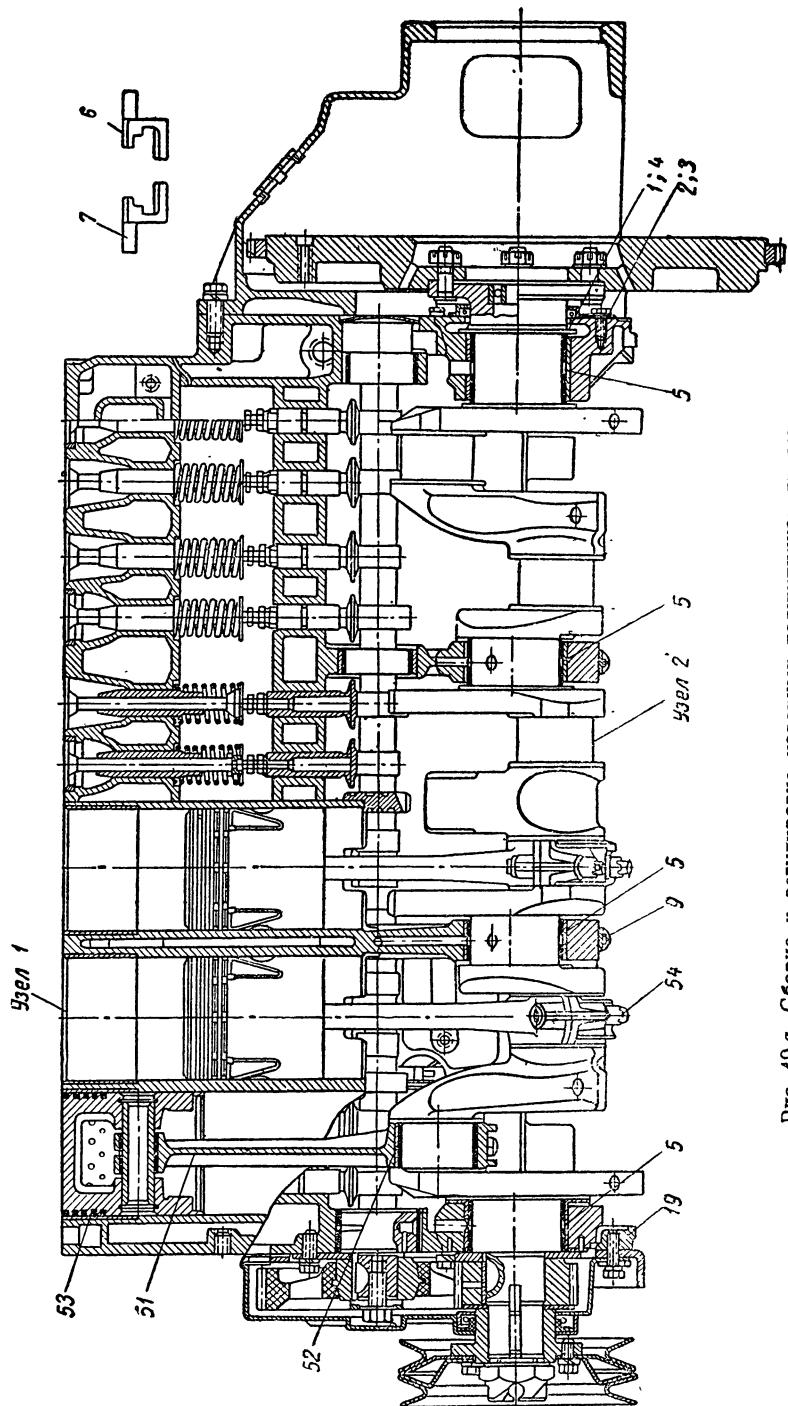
,а. Сборка и регулировка коренных подшипников двигателя
